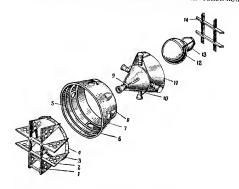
Элементы конструкции ҚА, предназначенного для маневра на орбите: 1 — типичный лонжерон для крепления элементов конструкции; 2 — нижние лонжероны; 3 — косыики; 4 верхнее усилнвающее кольцо; 5 — усиливающие кольца: 6 — нижнее кольцо; 7 — внешияя оболочка; 8 — верхнее кольцо; 9 — растяжки двигателя продольной тяги; 10 растяжки двигателя поперечной тяги; 11 — внутрениий конус; 12 — топливный бак; 13 — баллон сжатого газа; 14 — узел верхиих лонжеронов
